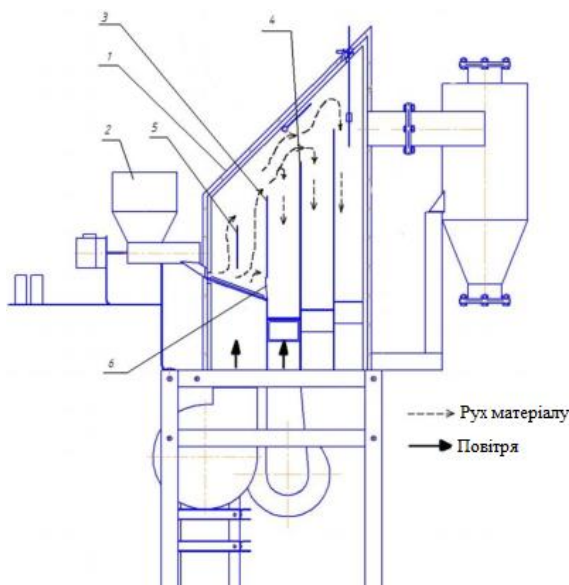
Схема лабораторно-експериментального пневмосепаратора для розділення зернового матеріалу : 1 - корпус; 2 - шнековий дозатор; 3 - задня стінка сепаруючого каналу; 4 - стінка осаджувального каналу; 5 - бар'єр, що вирівнює зерновий потік; 6 - перегородка
